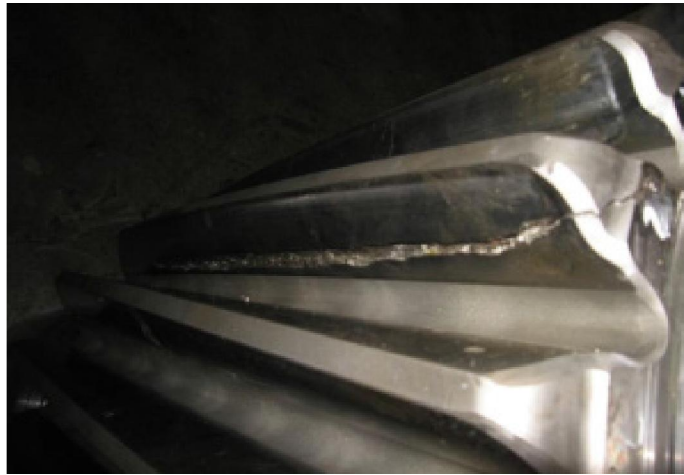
Fissuration ou cracks "Engrenages"
